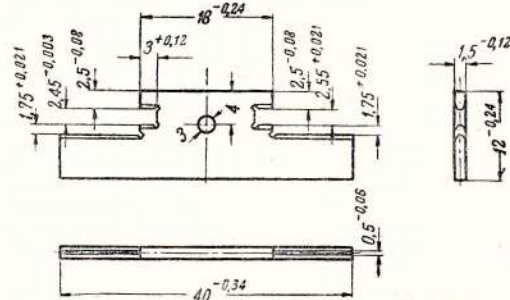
Шаблон для проверки расположения канавки на ролике К-25 и К-А
